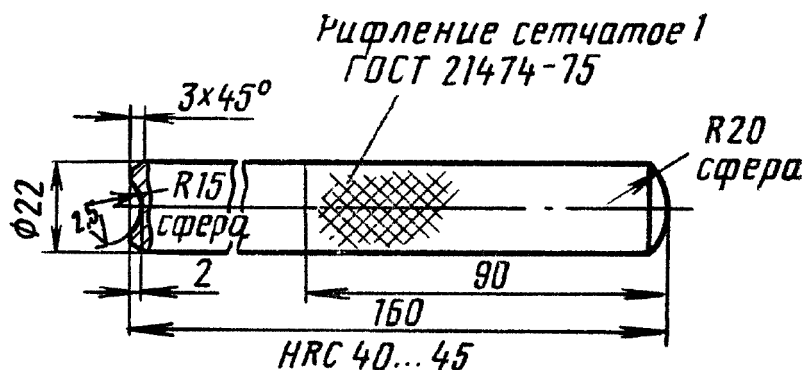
Боек для запрессовки заглушек в отверстия под пружину стопорного шарика в корпусе коробки передач
